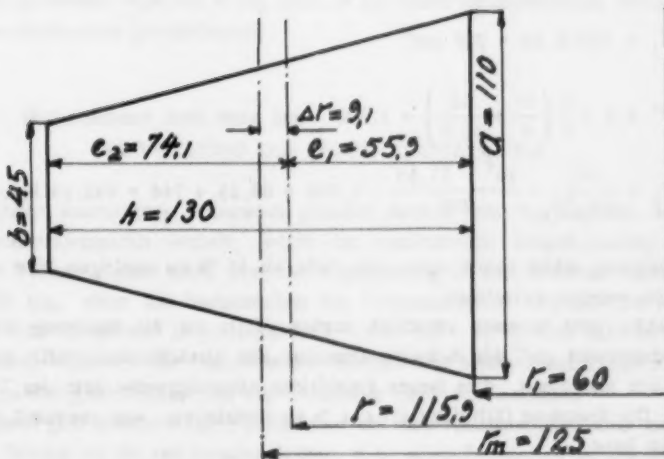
Horizontalschnitt durch einen Lasthaken mit reinem Trapezprofil.
